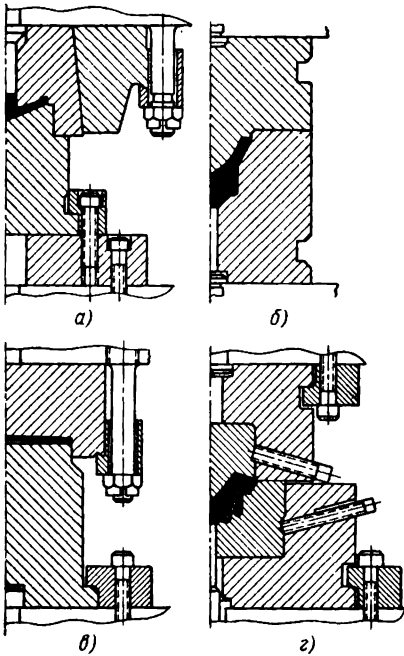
Схема конструкций штампов, применяемых на высокоскоростном молоте фирмы «U. S. I.»: а — для турбинного диска; б — для ступицы; в — для плиты; г — для буровой коронки
